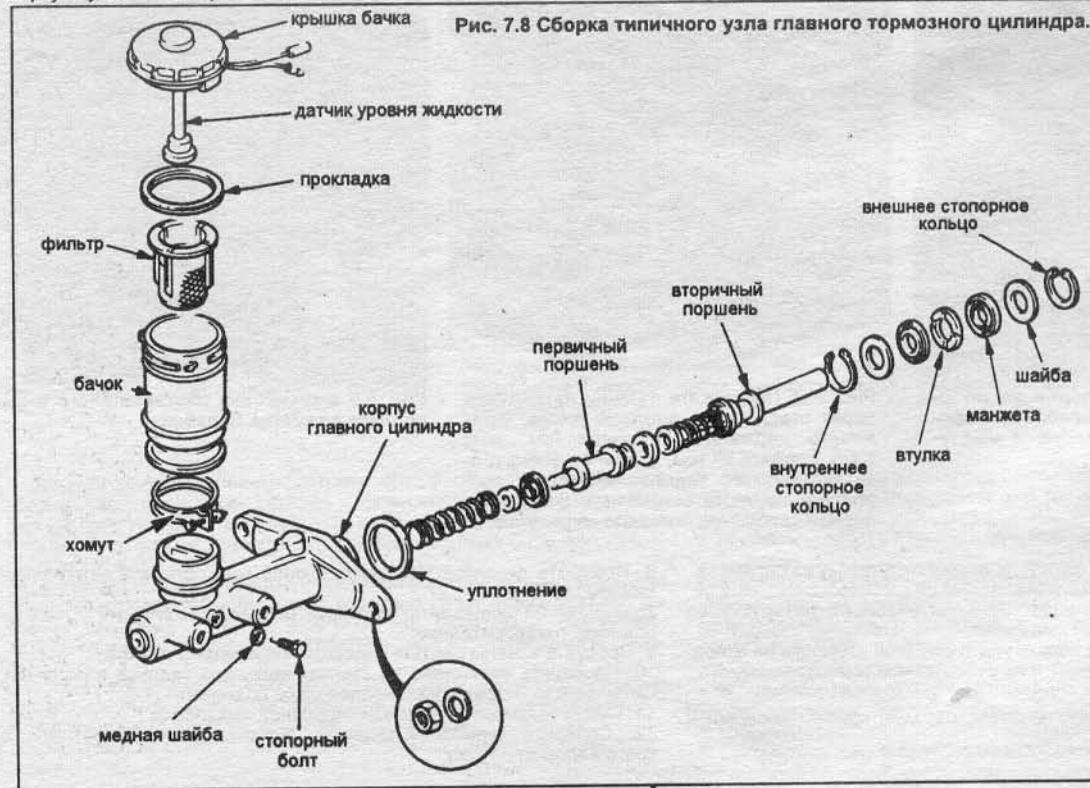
Сборка типичного узла главного тормозного цилиндра.
